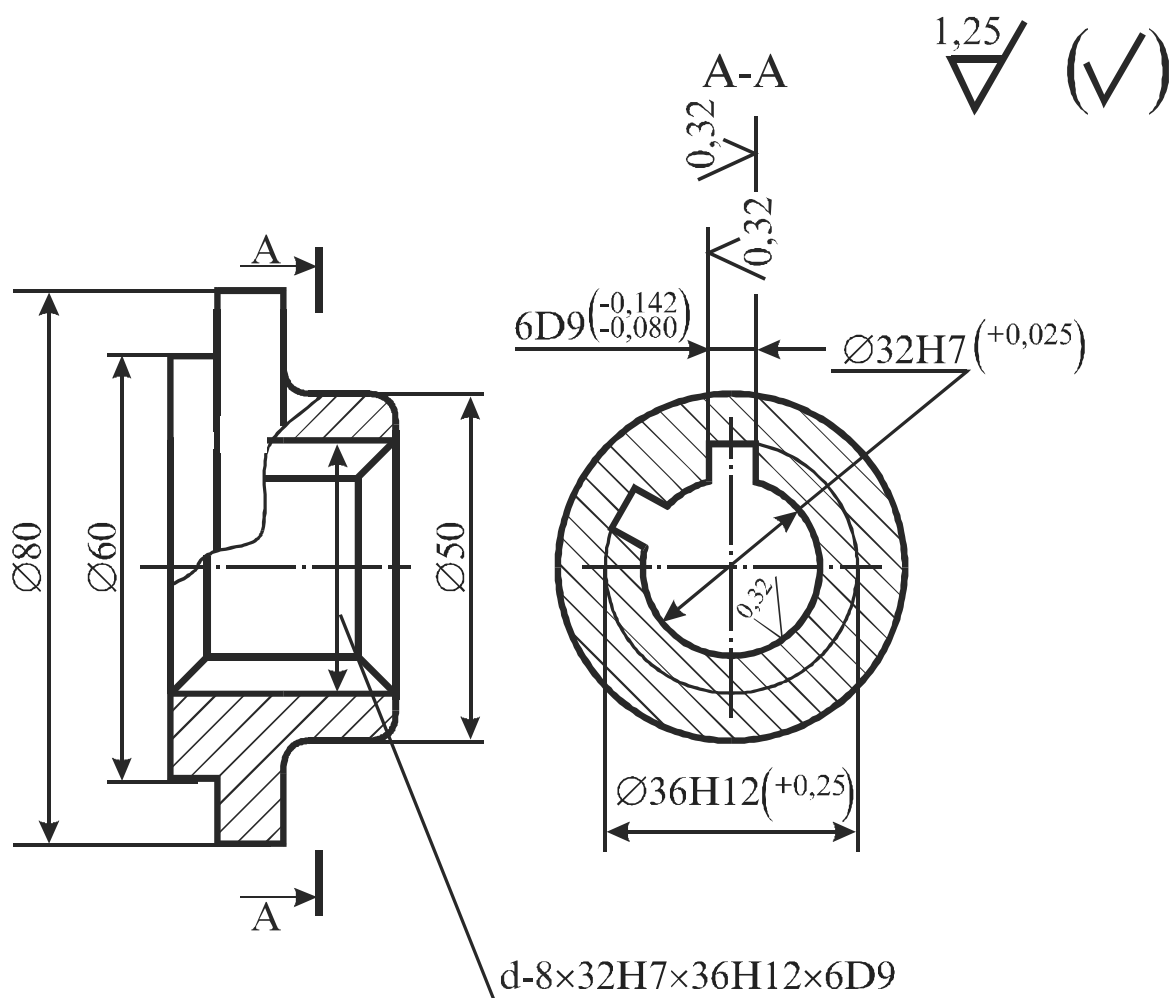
Пример оформления рабочего чертежа шлицевой втулки
